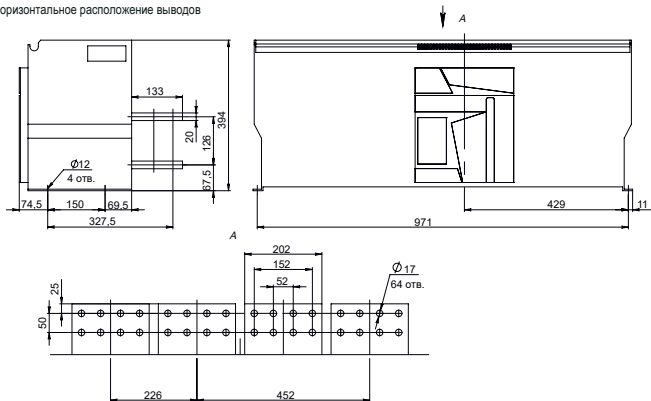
Габаритные размеры стационарных трехполюсных выключателей типоразмера Н
